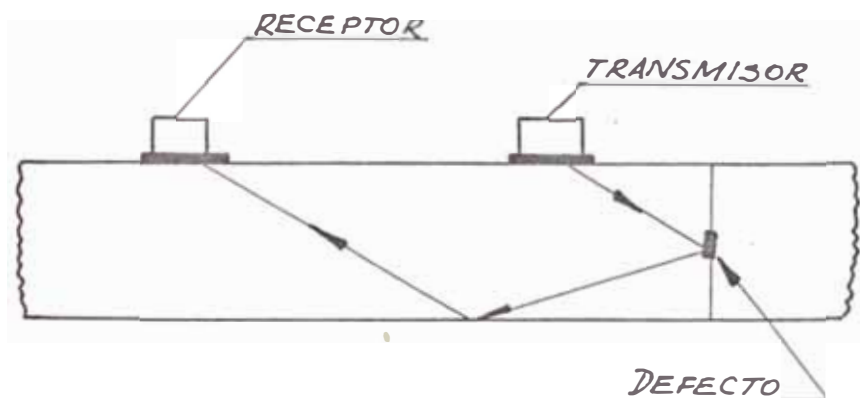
Utilización de sondas de onda transversal para localizar un defecto de una soldadura a tope.
